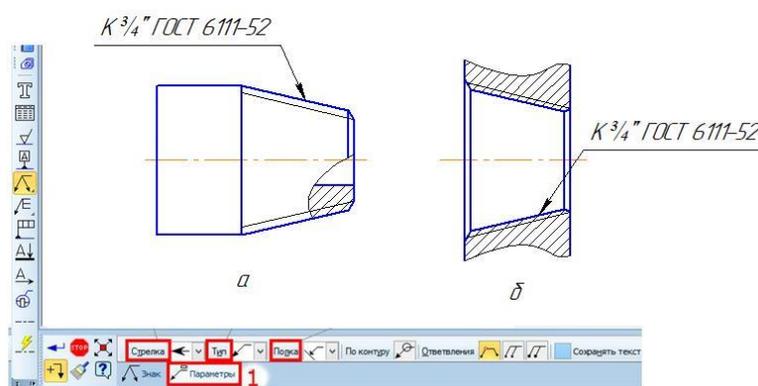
Обозначения наружной и внутренней конической дюймовой резьбы
